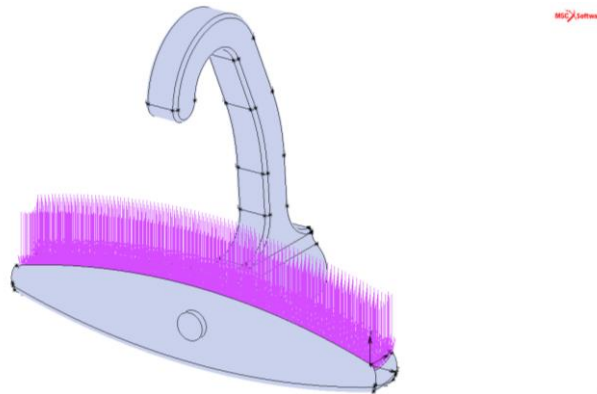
Aplicación de las cargas verticales provocadas por la curdina
